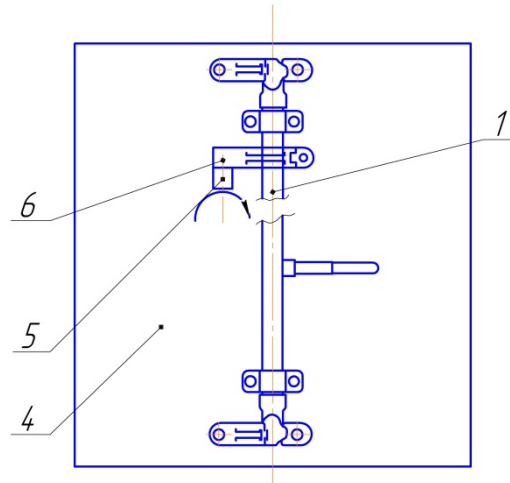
Запірний пристрій кулачкового типу: 1 – штанга; 4 – частина дверей; 5 – вертикальний гвинтовий замок; 6 – скоба.
